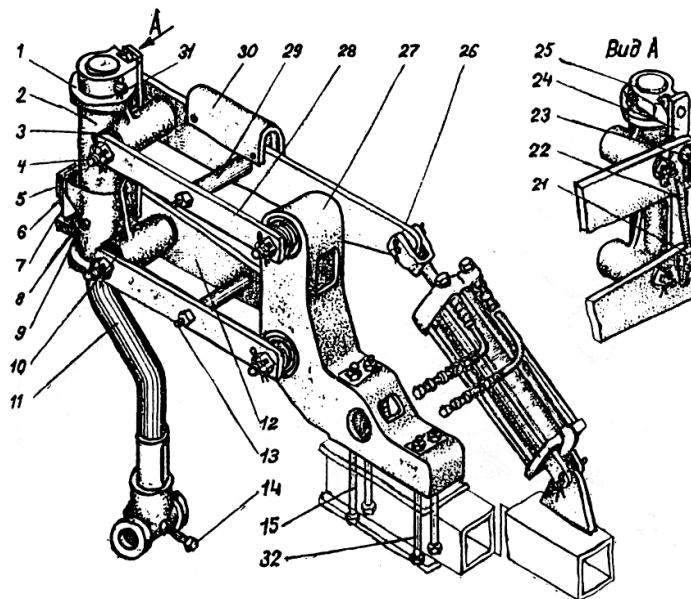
Механизм переднего бороздного колеса: 1 – направляющие кольца; 2 – верхний стакан; 3 – шайба; 4 – палец с корончатými гайками шайбами и шплинтами; 5 – прокладка; 6 – стопорная планка; 7 – пружина с роликом, болтом, шайбой и шплинтом; 8 – масленка; 9 – нижний стакан; 10,29 – втулки; 11 – ось; 12,28 – рычаг; 13,15,32 – болт с гайкой и шайбой; 14 – болт с контргайкой; 21,27 – кронштейн; 22 – пружина; 23 – палец с корончатой гайкой, шайбой и втулками; 24 – планка; 25 – ролик с запорным кольцом; 26 – водило; 30 – упор с болтами и шайбами; 31 – чека со шплинтом
